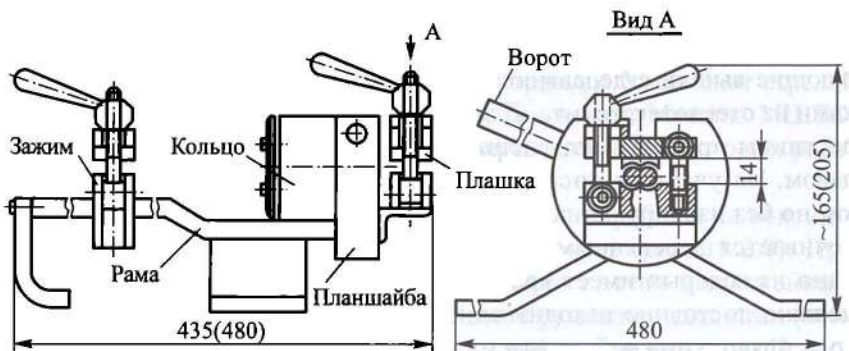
Приспособление для скручивания трубчатых овальных соединителей
